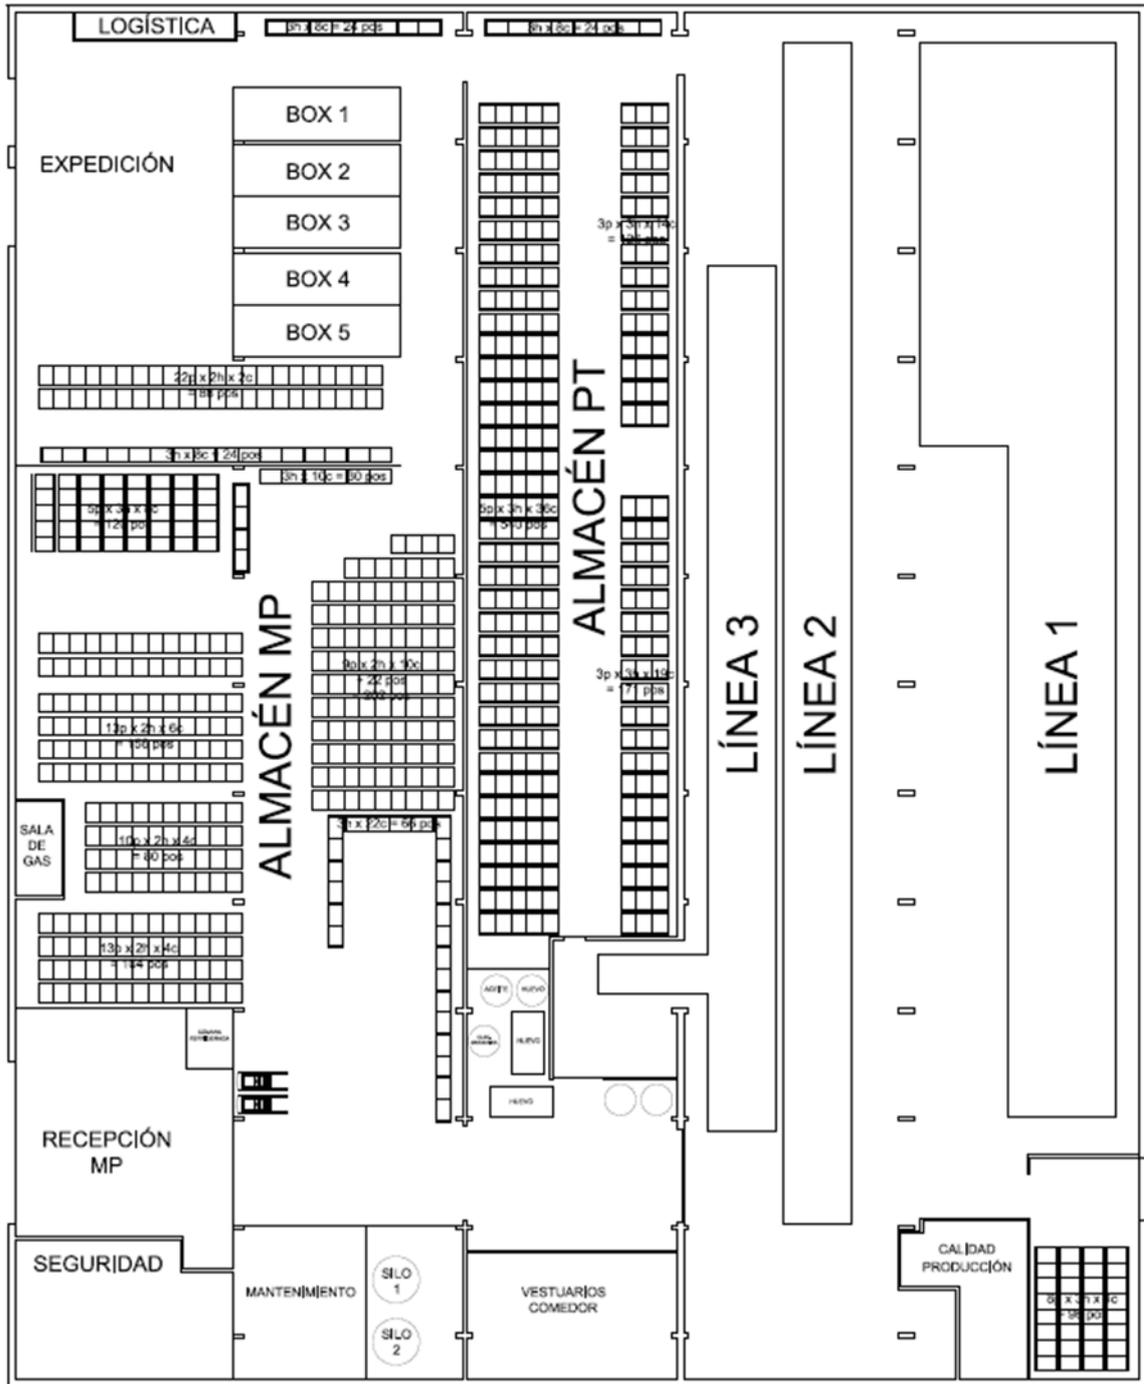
Layout de planta actual. Fuente: Elaboración propia.
